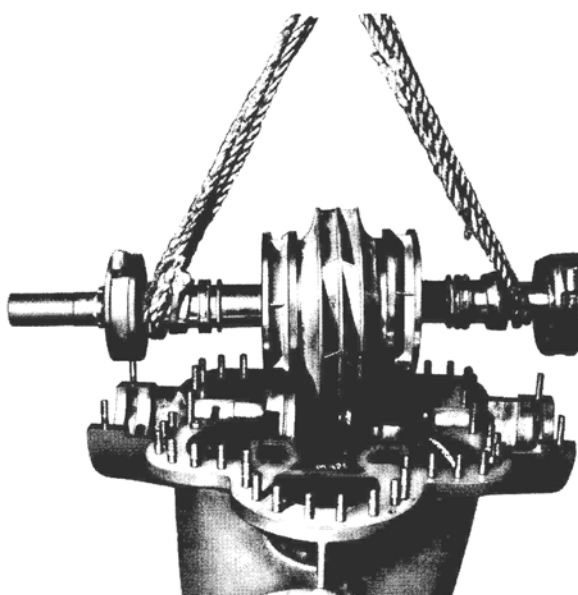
Levantamento e extração do conjunto girante de dentro do corpo inferior
